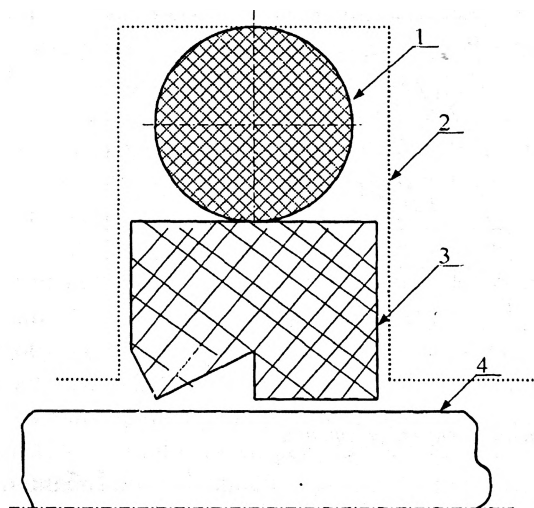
Принципиальный вид комбинированного резино-пластмассового уплотнения штока. 1 – резиновое кольцо, 2 – посадочная канавка штоковой втулки, 3 – фторопластовое уплотнение, 4 – шток
